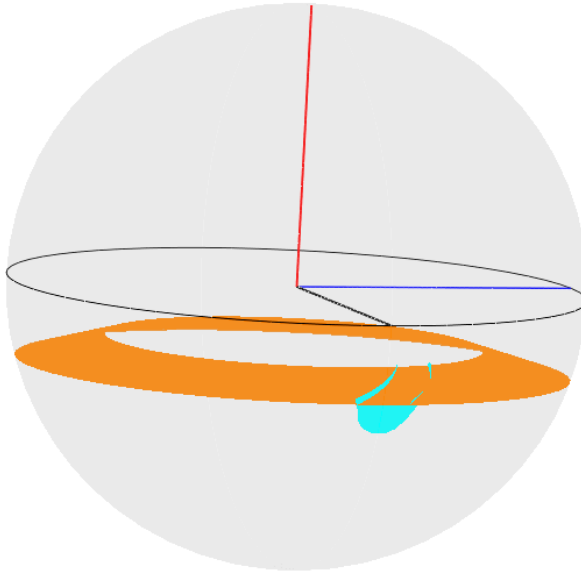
Фрагмент зуба поверхности колеса и «обрезающий» конус
